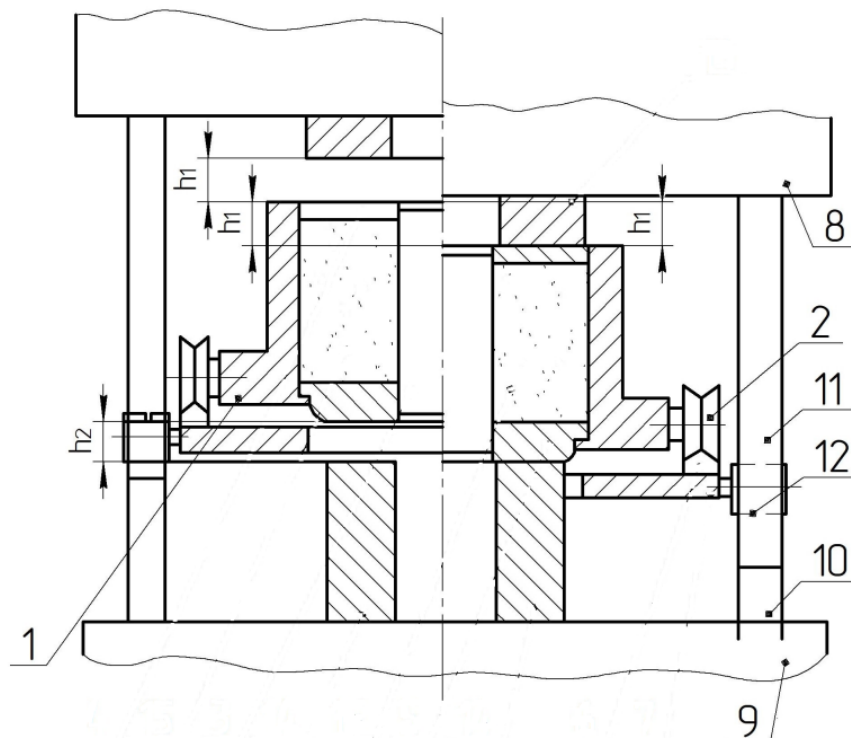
Исходное и начальное перед прессованием положения пуансона пресса и пресс-формы для двухстороннего прессования (вид спереди)
